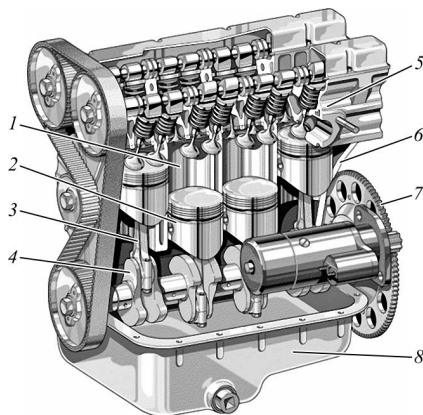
Схема рядного четырехцилиндрового двигателя жидкостного охлаждения: 1 – цилиндр; 2 – поршневая группа; 3 – шатун; 4 – коленчатый вал; 5 – головка цилиндров; 6 – блок-картер; 7 – маховик; 8 – поддон картера
